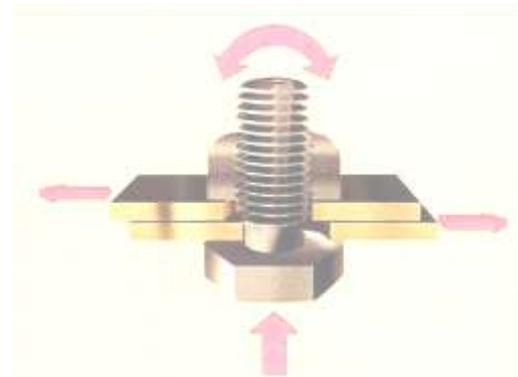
Esfuerzos que producen relajación y autoaflojamiento en unión atornillada.
